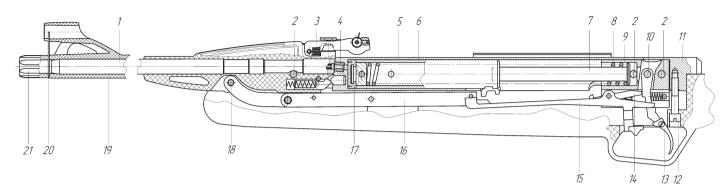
Схема механизмов винтовок МР-512, МР-512М с комбинированной ложей
